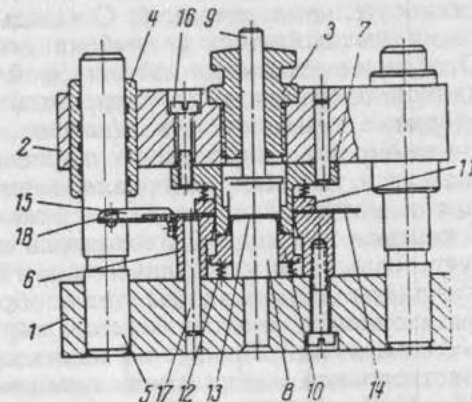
Штамп вырубki и первой вытяжки корпуса цоколя.
